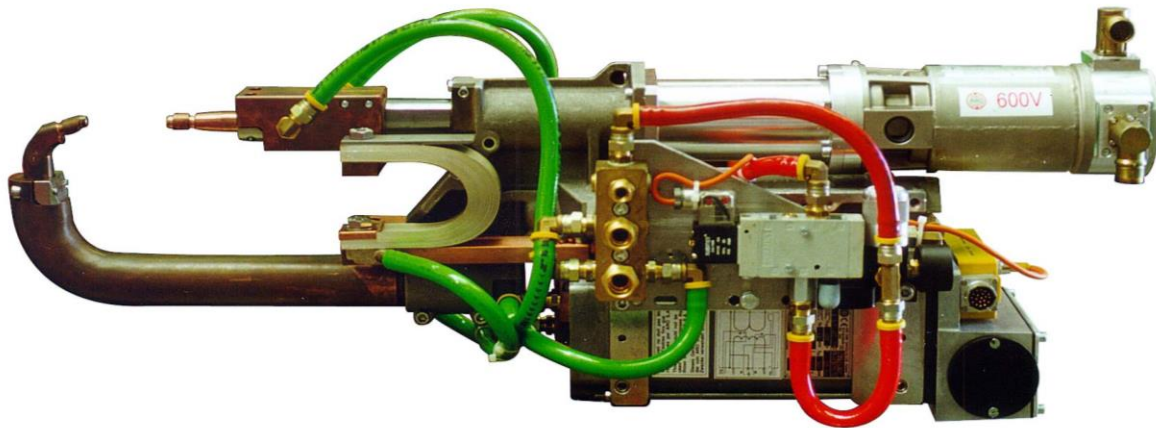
Pistola de soldadura por puntos de resistencia. Fuente: TWI
